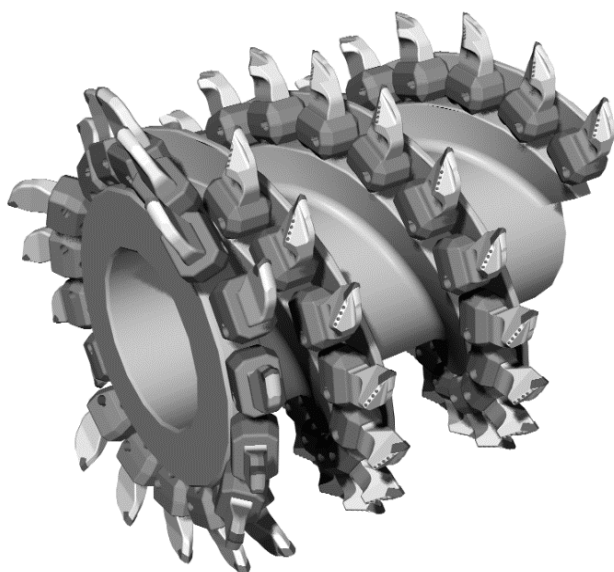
Схема расположения режущего инструмента с рабочей боковой гранью на шнеке
